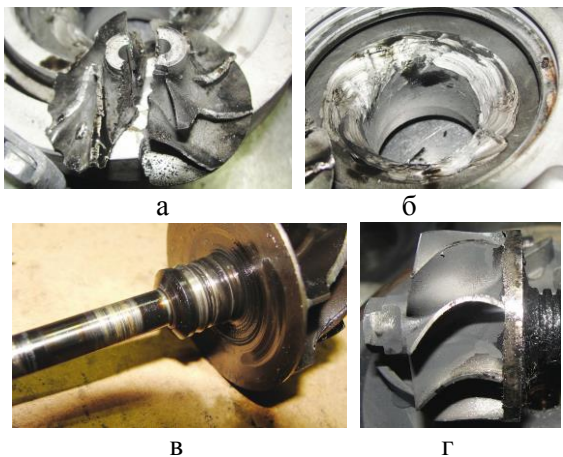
Разрушенное колесо компрессора: а – поврежденный корпус; б – перегрев и повреждение подшипников, вала; в – перегрев и повреждение лопаток турбины; г –
